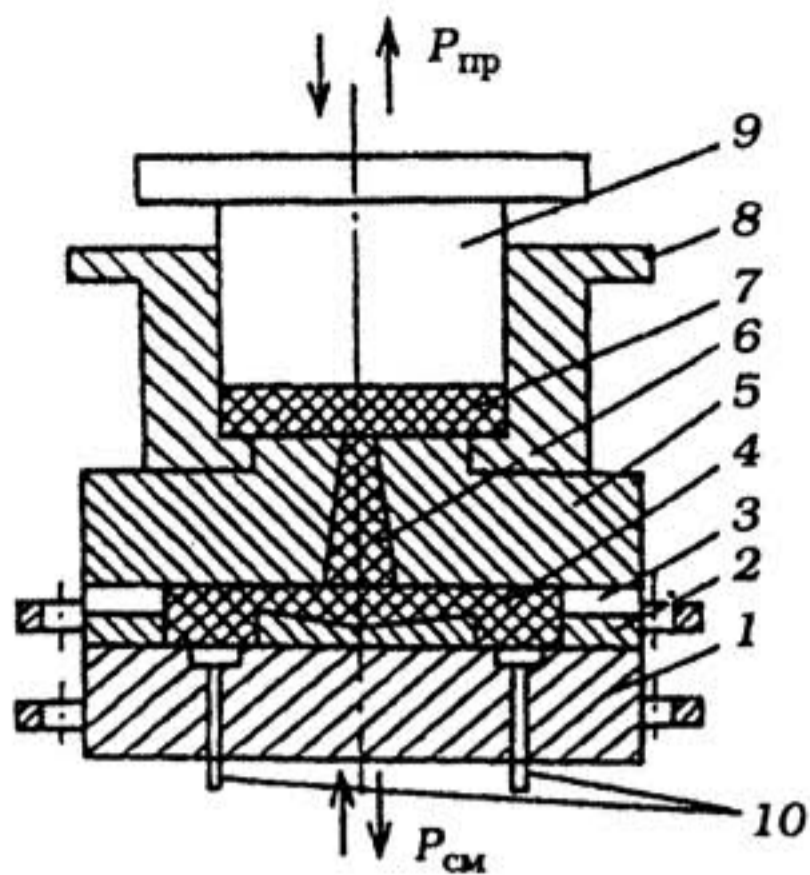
Схема изготовления тары методом литьевого прессования: 1 — нижняя плита; 2 — матрица; 3 — воздушные каналы; 4 — изделие; 5 — верхняя плита; 6 — литниковые каналы; 7 — пресс-остаток; 8 — загрузочная камера; 9 — шток; 10 — выталкиватель
